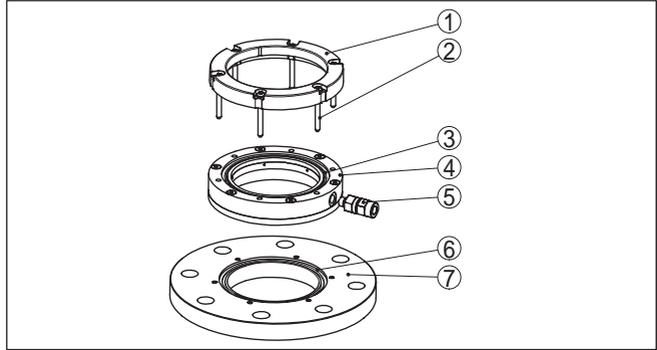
Montaggio dell'attacco per spurgo con flangia di adattamento
